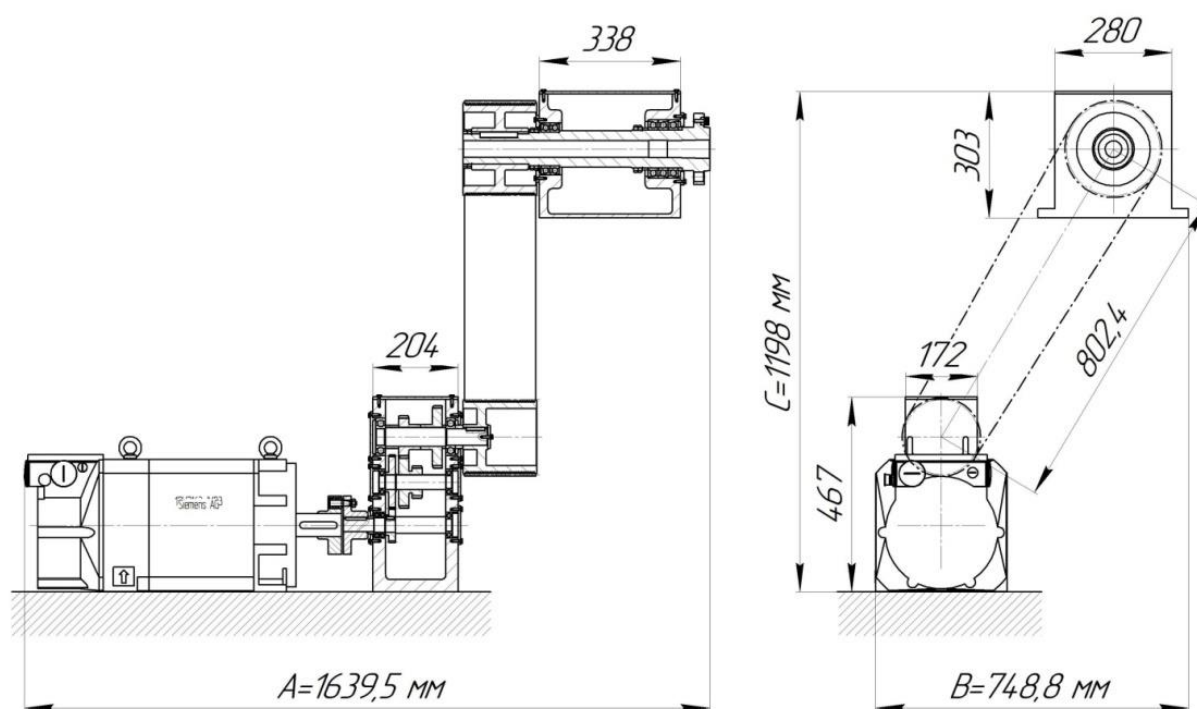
Габаритные размеры привода главного движения варианта компоновки № 2
